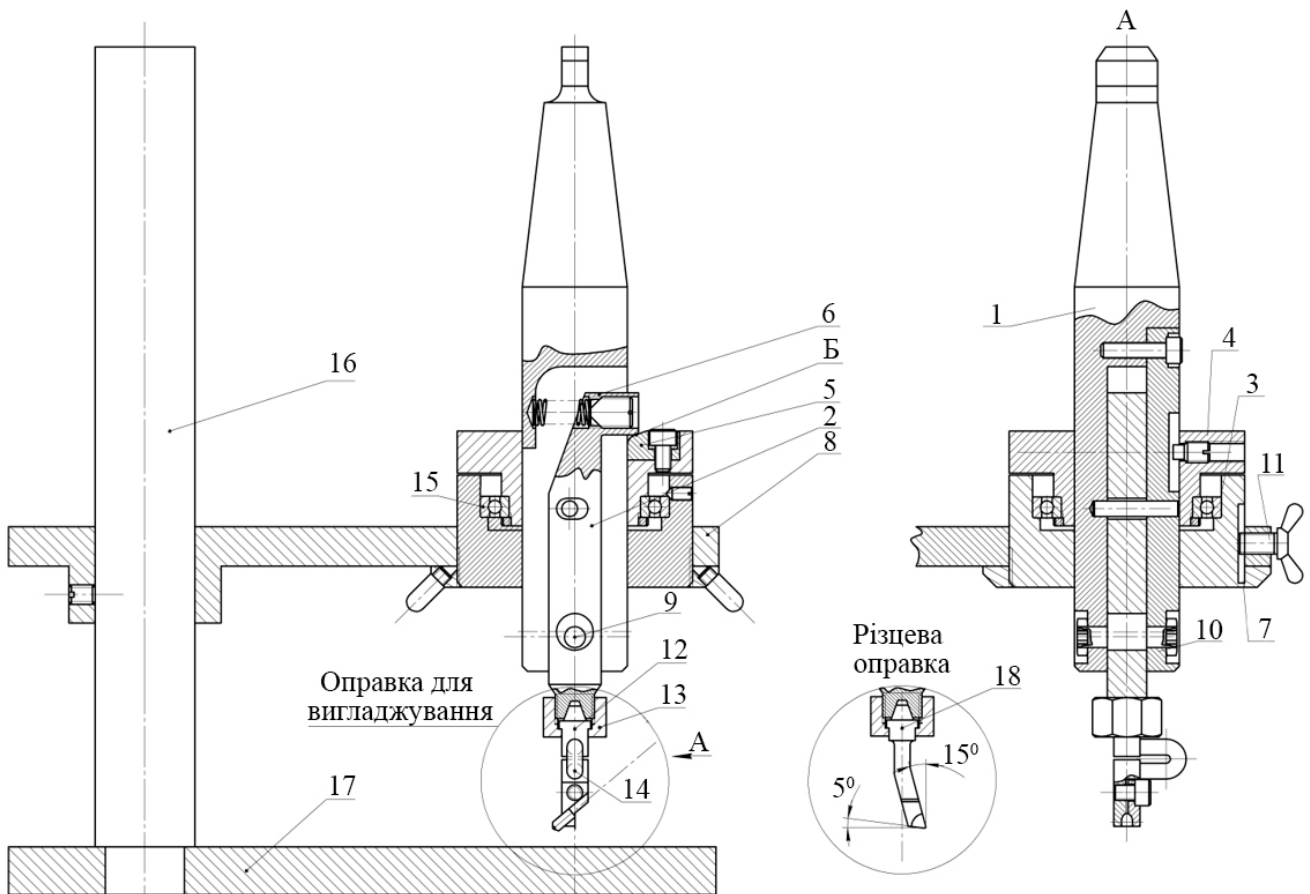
Пристрій для обробки та зміцнення поверхні переходу отвору у площину алмазним вигладжуванням: 1 – оправка; 2 – коромисло; 3 – корпус; 4 – втулка; 5 – копір; 6 – пружина; 7 – лімба; 8 – стійка; 9 – ексцентрик; 10 – гайка; 11 – гвинт; 12 – оправка для вигладжування; 13 – гайка; 14 – пружний елемент; 15 – підшипник; 16 – стійка; 17 – основа; 18 – різцева оправка.
